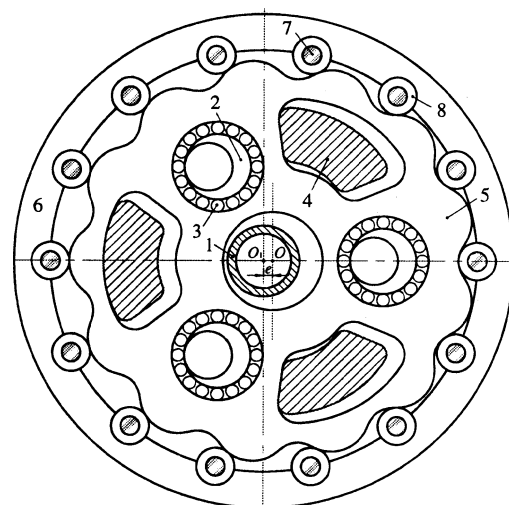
Поперечное сечение редуктора: 1 – входной вал; 2 – эксцентриковые валы; 3 – ролики подшипника; 4 – пальцы выходного вала; 5 – сателлит; 6 – обойма; 7 – втулки; 8 – цевки
